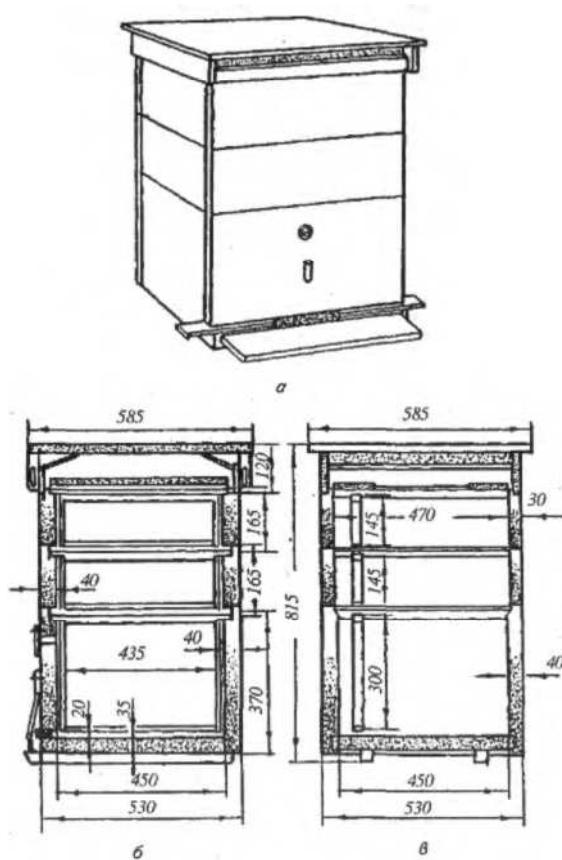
2. Двухкорпусный улей: а — общий вид; б, в — в разрезе (размеры в мм)
